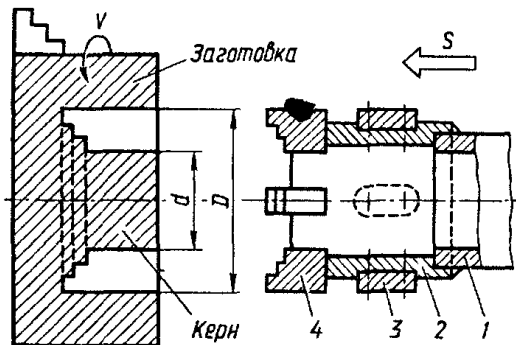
Кільцеве („трепануюче”) свердло: 1 - трубчастий подовжувач; 2 - трубчастий корпус; 3 - твердосплавна напрямна вставка; 4 - вставний зубець
